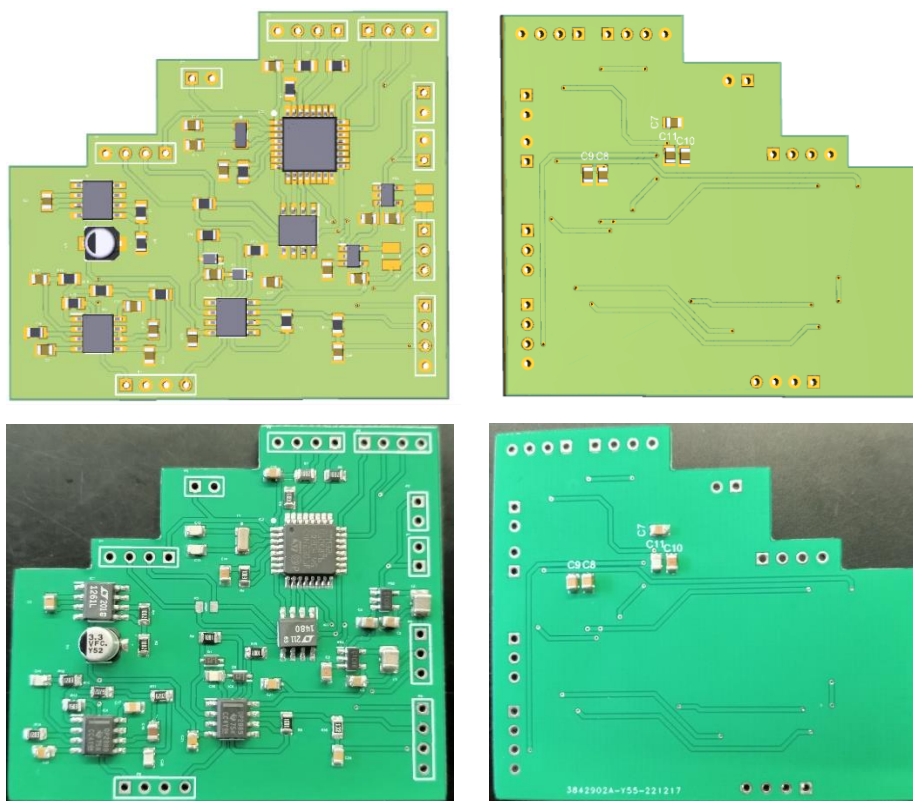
PCB (lado esquerdo Top Layer e do lado direito Bottom Layer)
